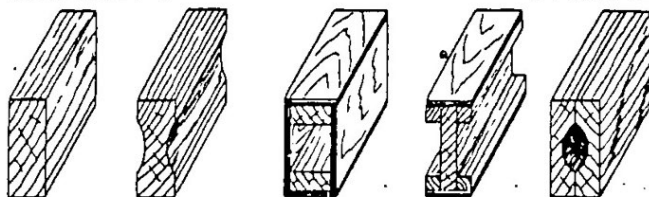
Tipos de longarinas construídas em madeira.
